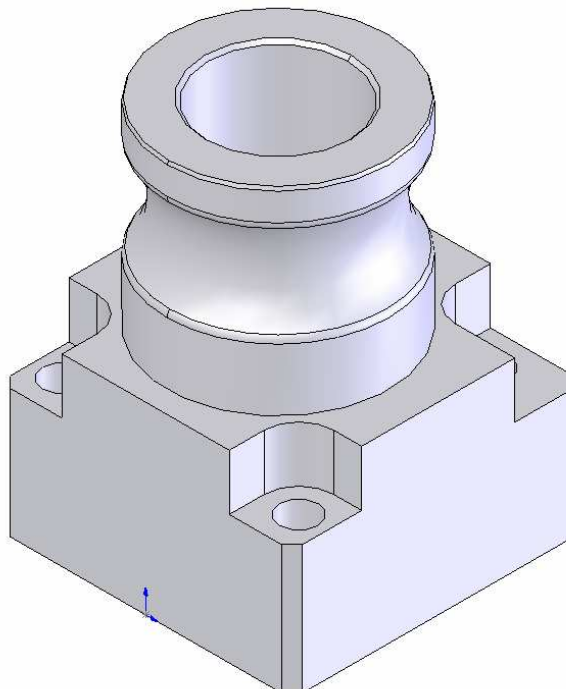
Dibuix en tres dimensions de la peça 3. Solidworks ®
